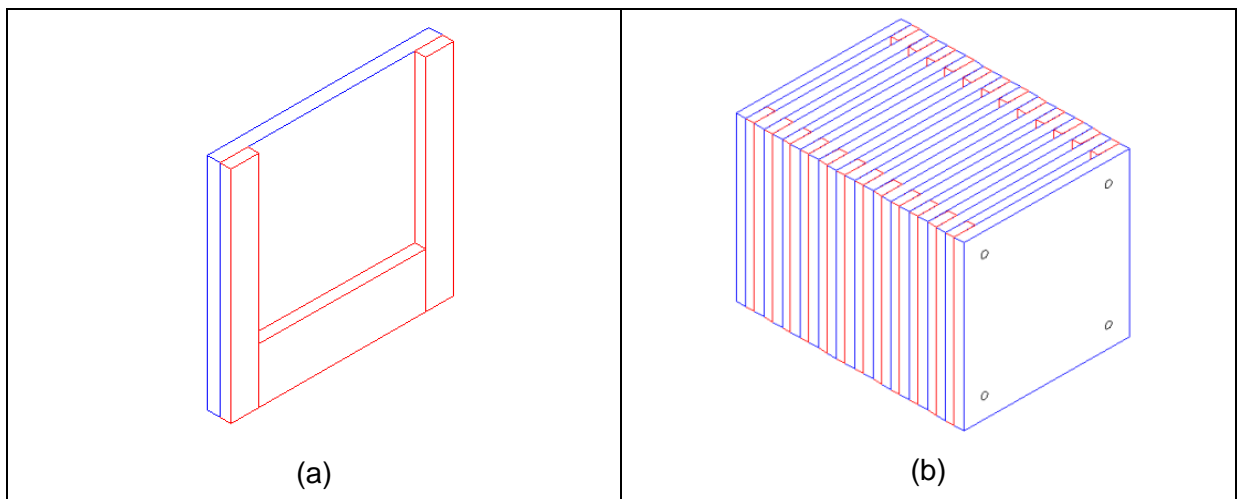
(a) Desenho do molde de cada placa; (b) Desenho da fôrma completa – bateria;
